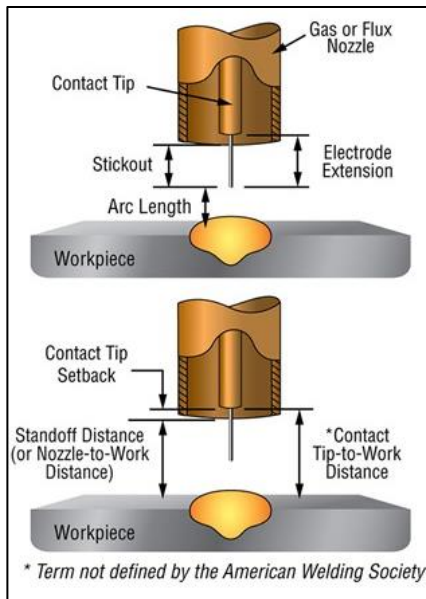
Définition des distances torche-substrat (millerwelds.com, 2019)
